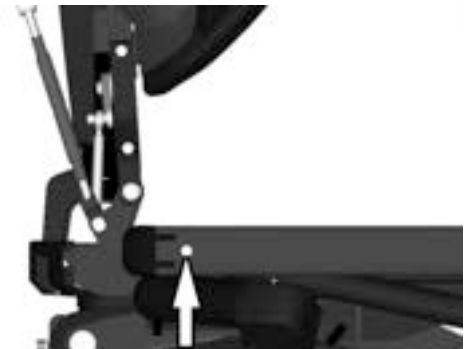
Hintere Befestigungsschraube der UniTrack-Schiene.
